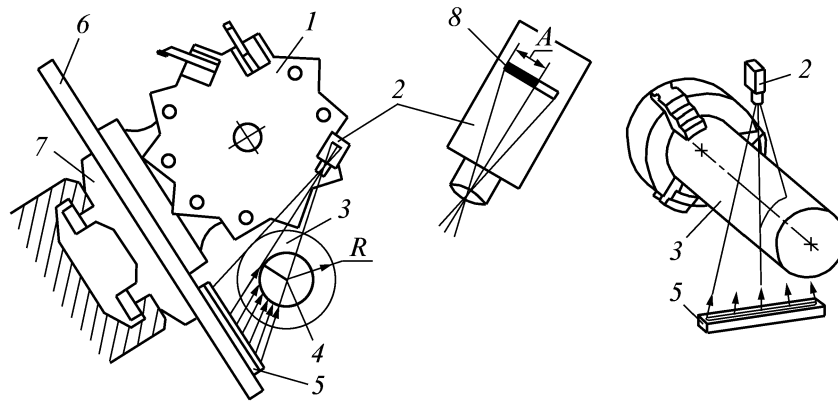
Схема расположения прибора в рабочей зоне токарного станка
